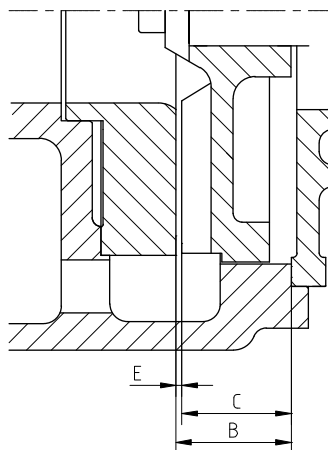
Зазор между крыльчаткой и износной пластиной, FRE группы подшипника 1.
